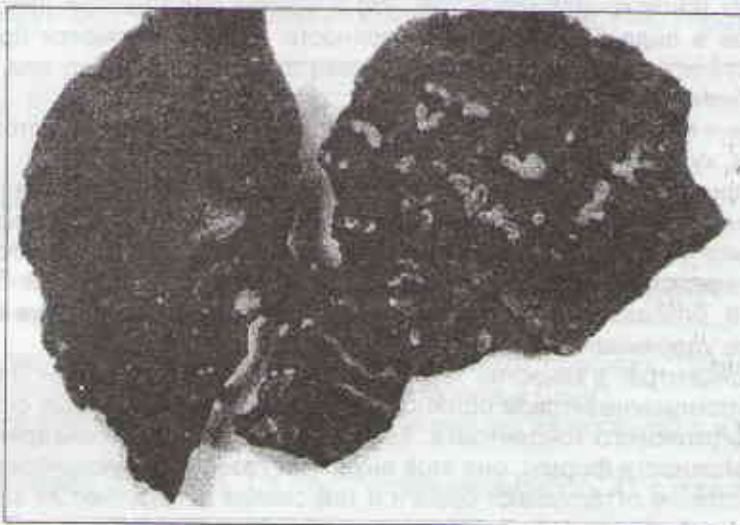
Пригарные корки с выступающими над ними складками, образовавшимися при отливке лопатки направляющего аппарата турбины для Каховской ГЭС
